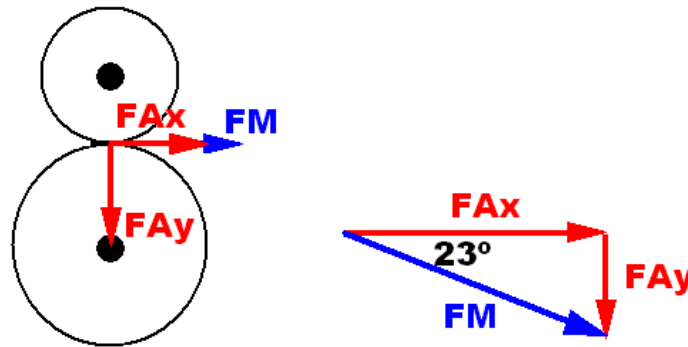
Fuerzas actuantes sobre los engranajes
